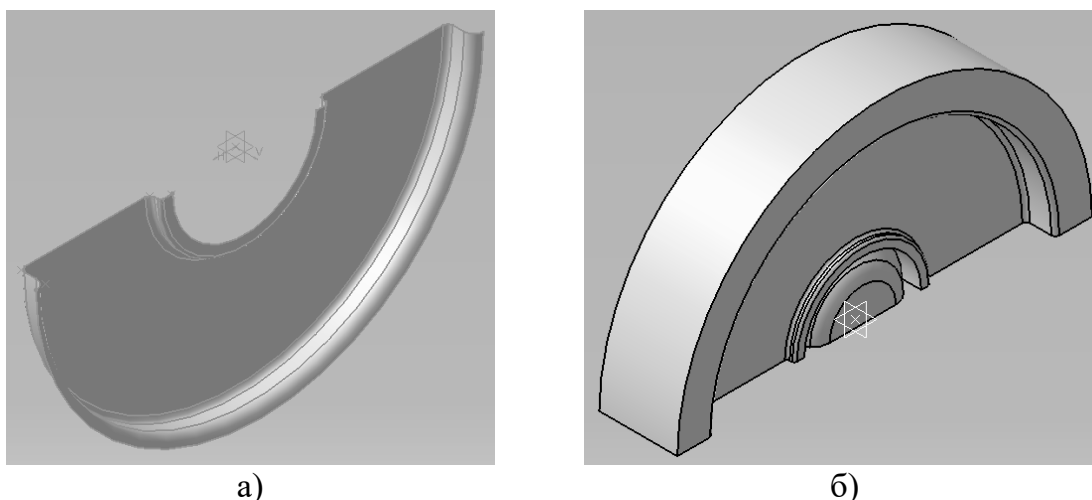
Деталь «крышка двигателя»: а) геометрическая модель детали, б) возможная матрица для штамповки при совмещенном комбинировании
